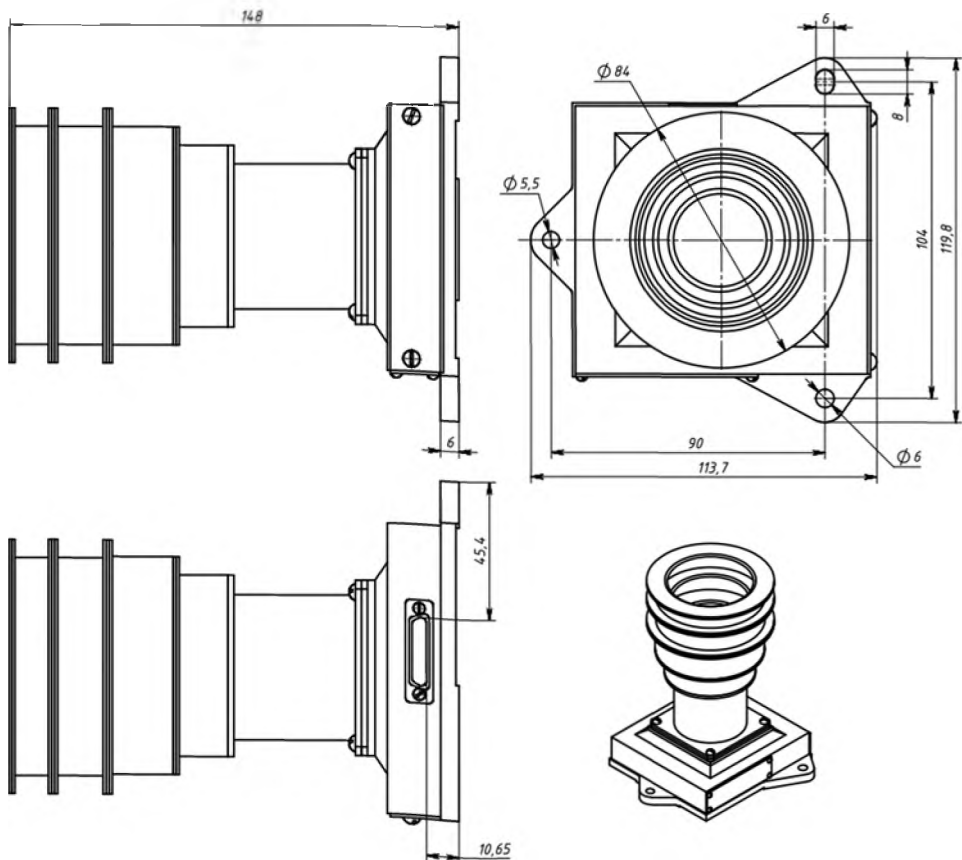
Габаритный чертёж звёздного датчика SXSRMINI_BOKZ01
